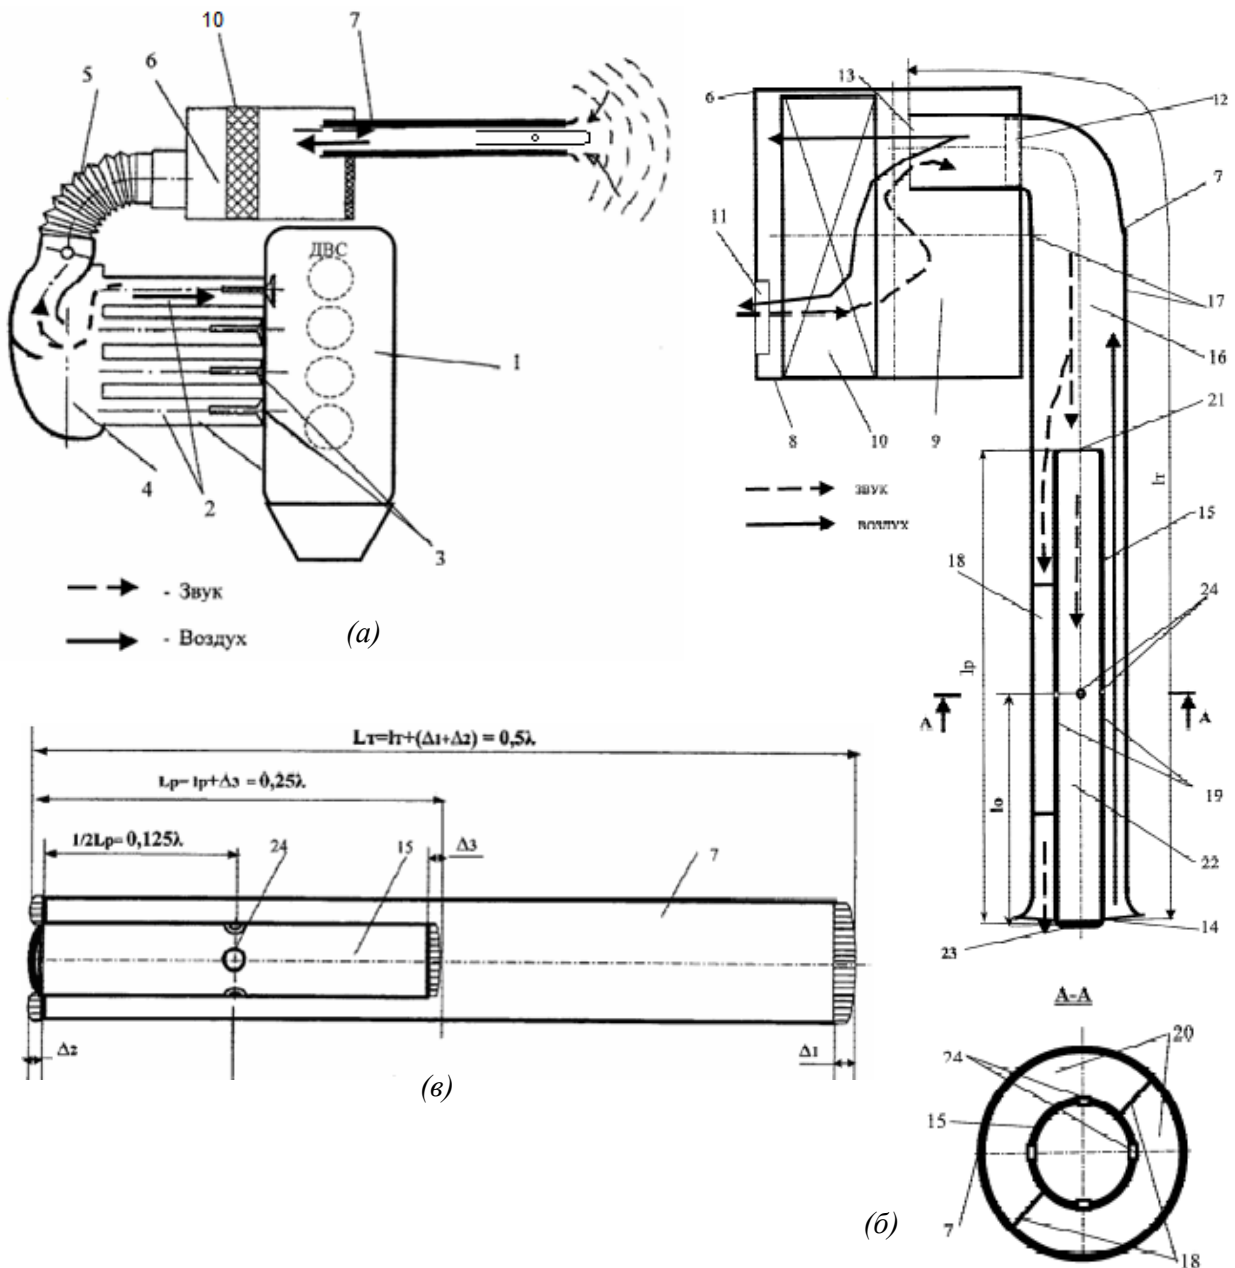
Схемы ДВС в сборе с системой впуска (а), воздухоочистителя (б) и продольного сечения воздухозаборного патрубка в сборе с четвертьволновым резонатором (в):
